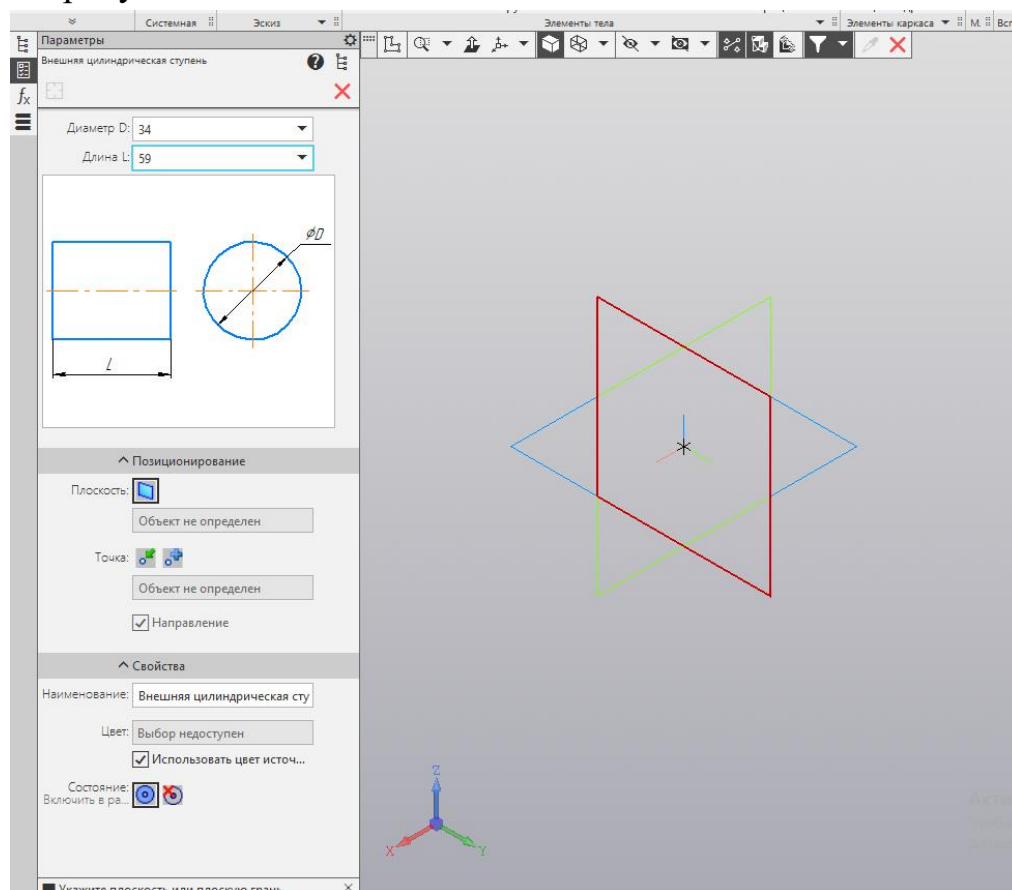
Ввод параметров внешней цилиндрической ступени вала-шестерни
